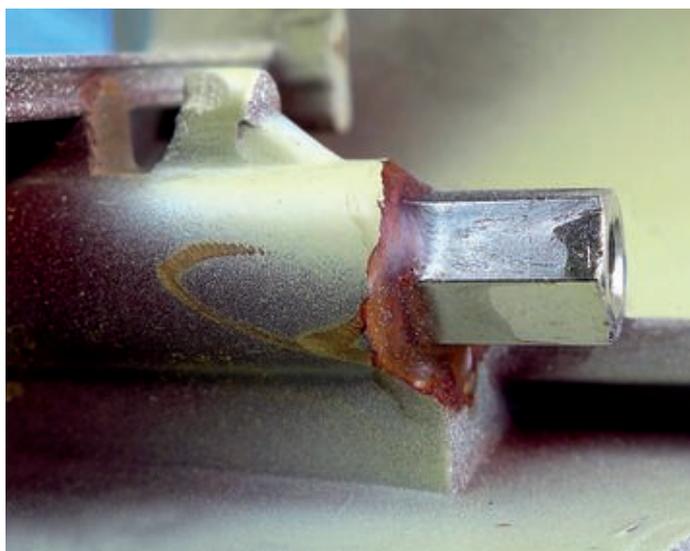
Die abgebrochene Aufnahme der Schraube rechts wurde durch einen Sechskant-Distanzbolzen ersetzt.
